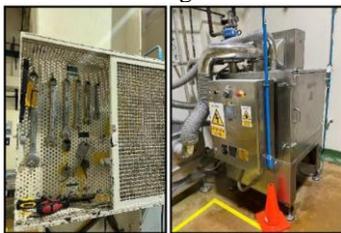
Cabina de Herramientas y de Lavado de Moldes
